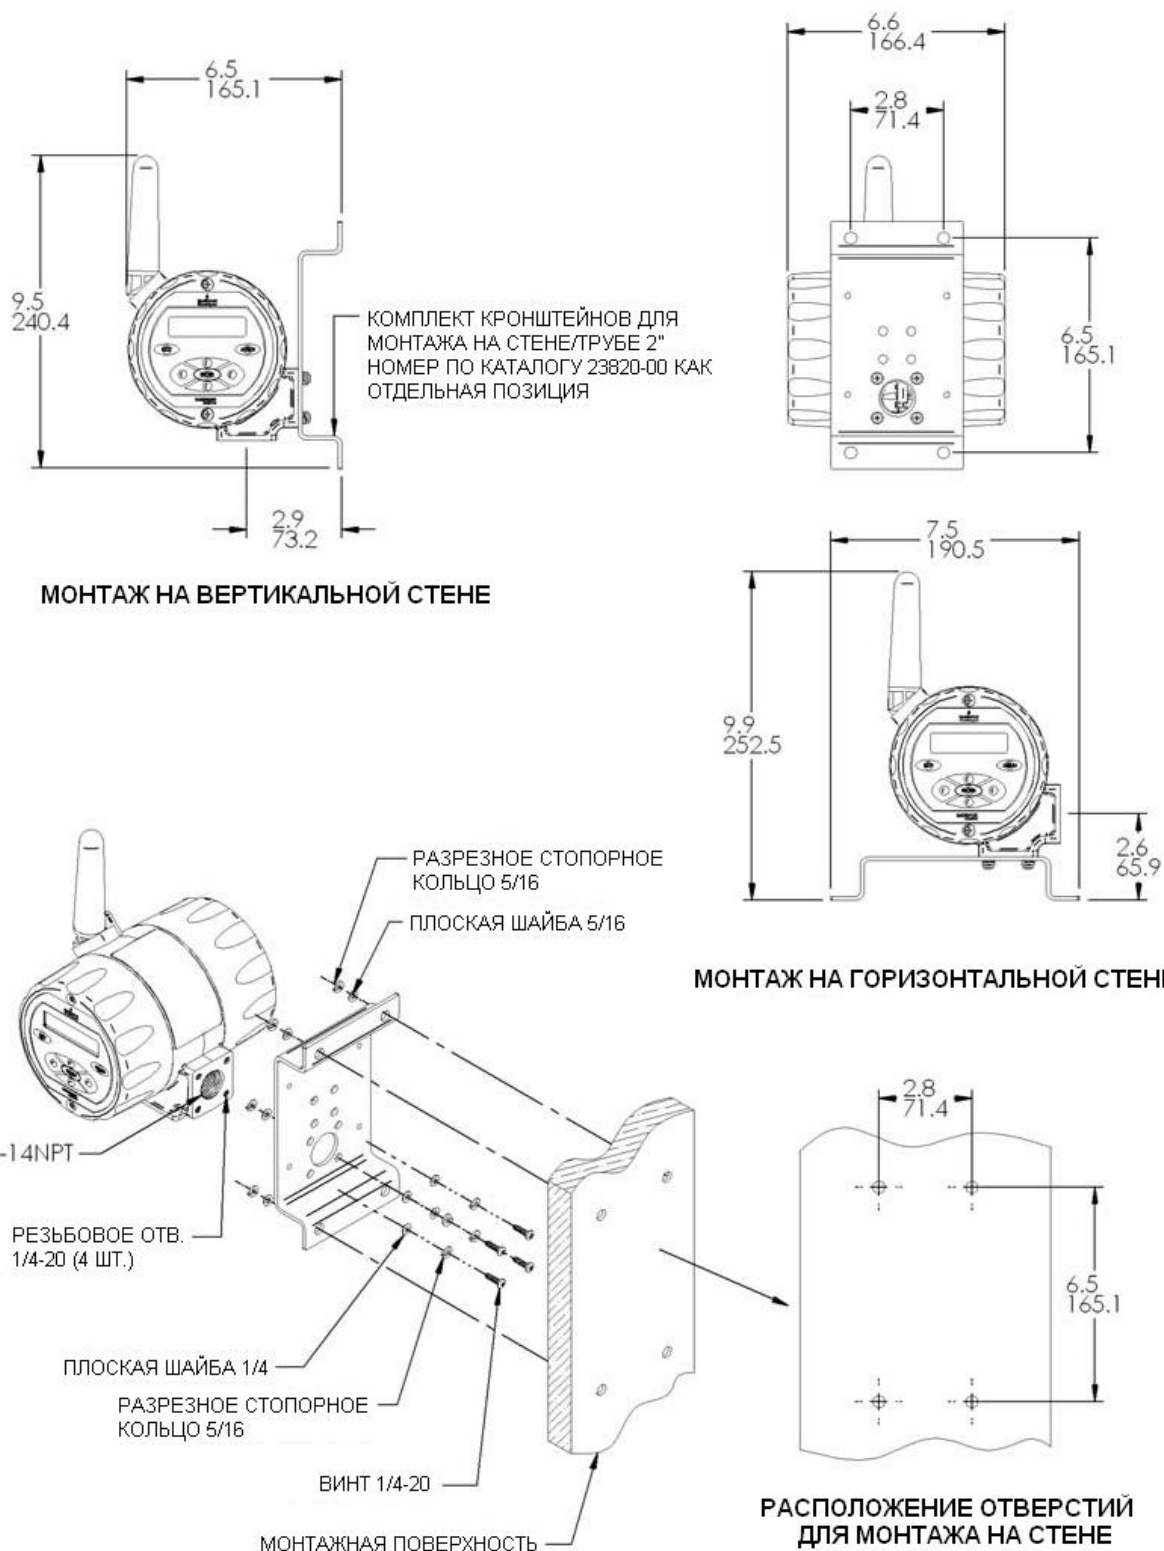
Установка датчика модели 6081 на стене. Используйте комплект монтажного кронштейна для установки на трубопроводе/стене, номер по каталогу 23820-00
